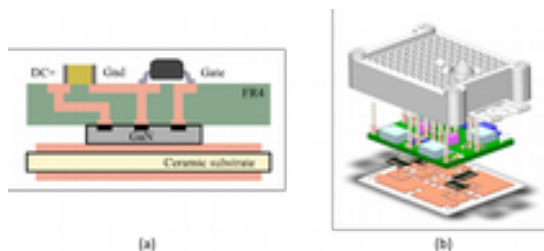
Exemple d'intégration de transistors GaN [3] : (a) vue en coupe (b) assemblage
